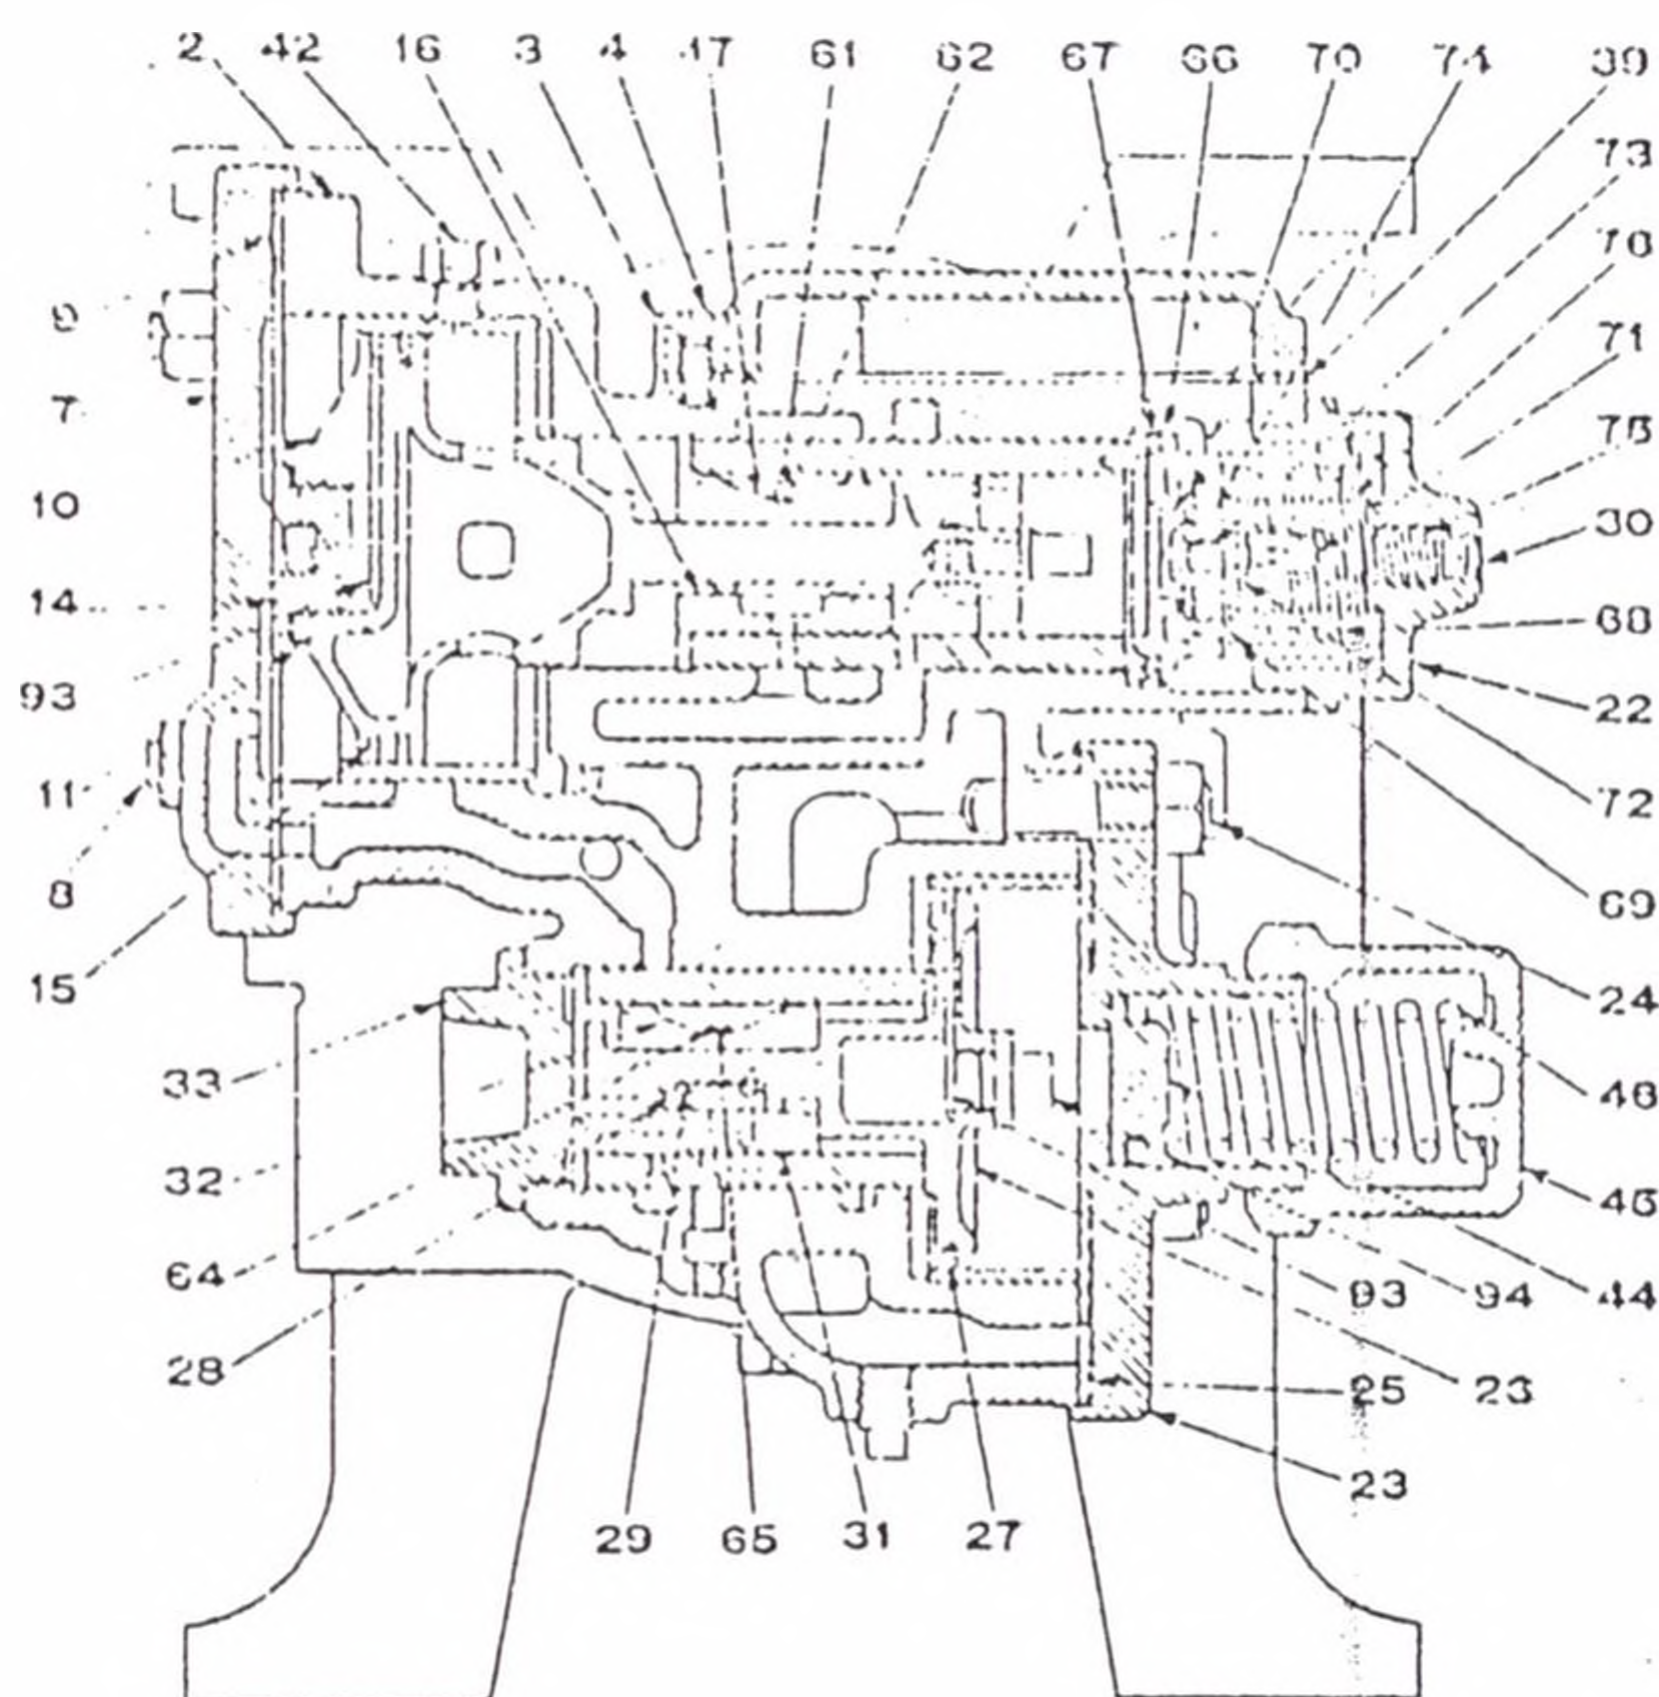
CONJUNTO DE LA VALVULA DISTRIBUIDORA 6-KR
